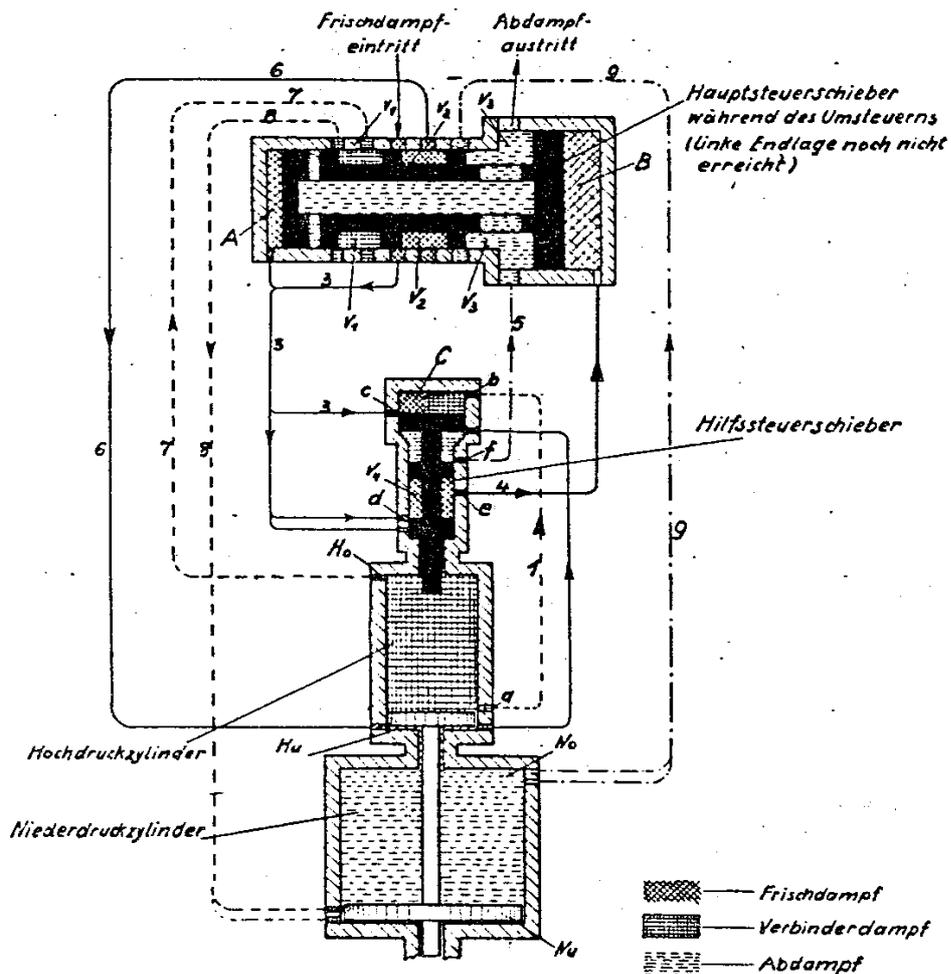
P-Steuerung (untere Totpunktlage der Arbeitskolben)
